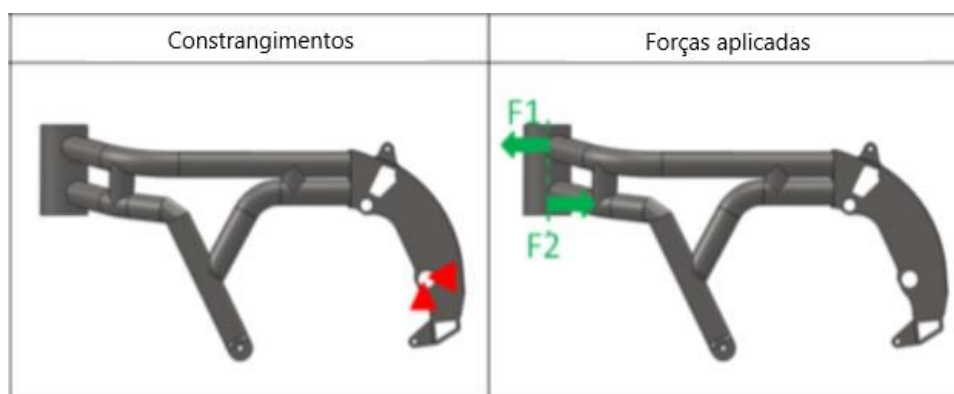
Constrangimentos e forças aplicadas (2)
